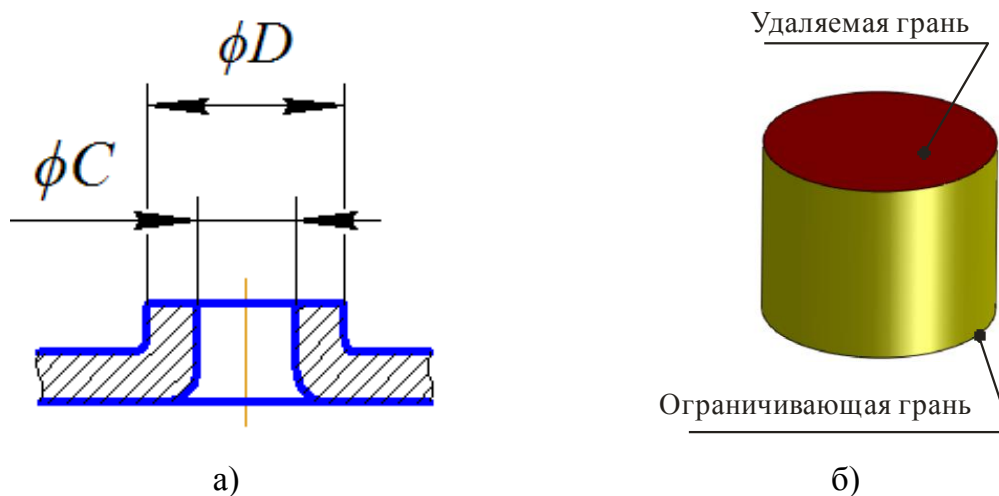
Вариант исполнения разбортовки в листовом металле для изготовления резьбы: а – чертеж разбортовки; б – инструмент формы
